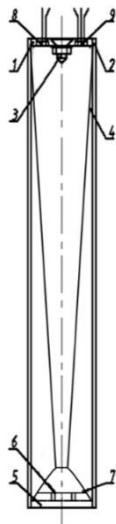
Схема ТТ: 1 – верхняя крышка; 2 – цилиндрический корпус ТТ; 3 – запорный узел; 4 – капиллярно-пористая вставка; 5 – нижняя крышка; 6 – инжекторные каналы; 7 – капиллярно-пористый испаритель; 8,9 – емкостные датчики конденсации, измеряющие толщину пленки жидкого конденсата.
